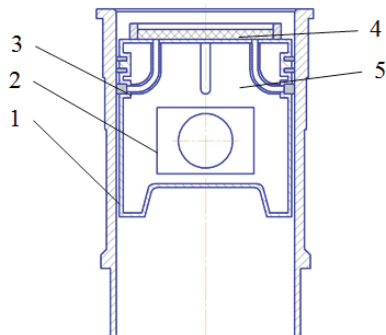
Схема смазывания рабочей поверхности гильзы цилиндра
